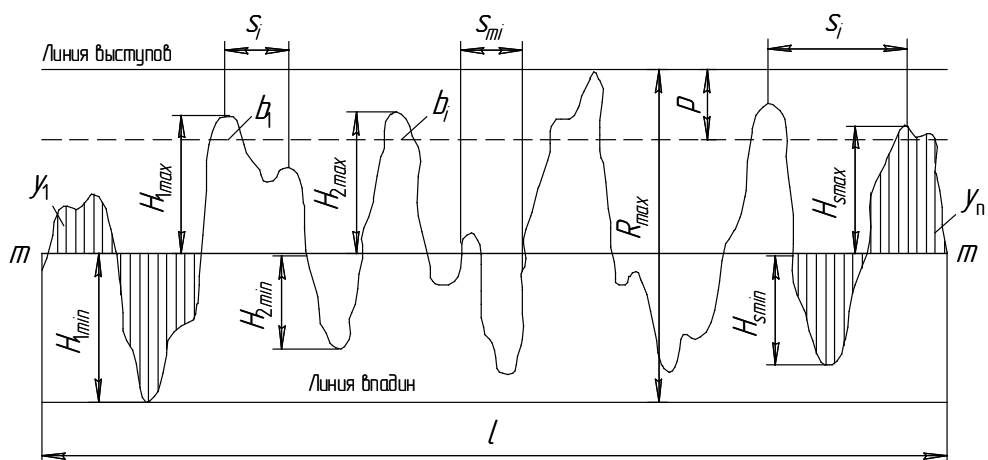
Профилограмма поверхности и основные параметры шероховатости [2]
